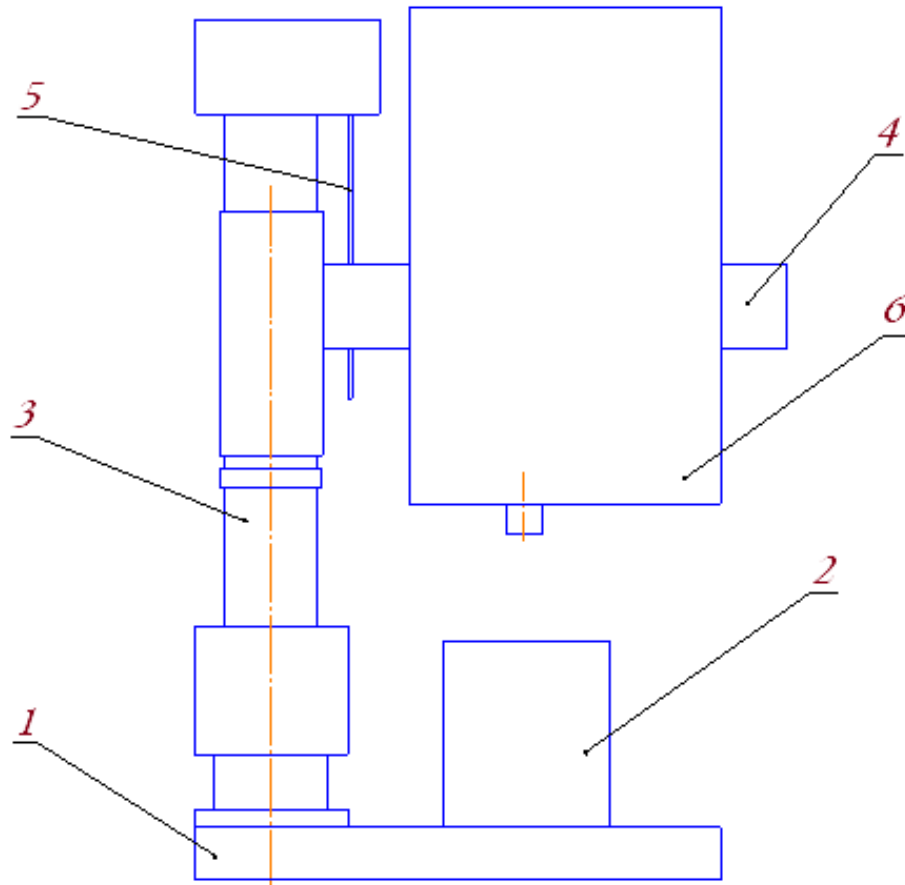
Компонувальна схема радіально-свердлильного верстата
